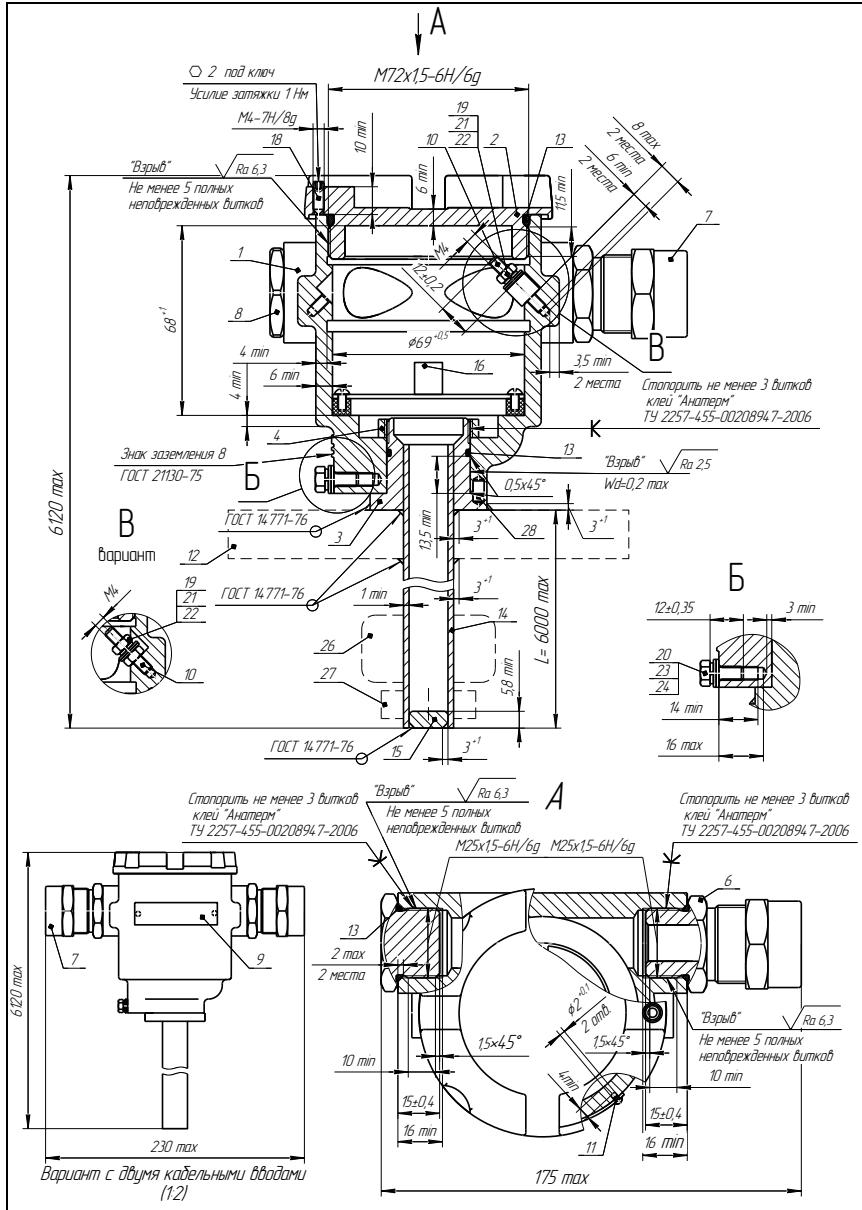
Чертеж средств взрывозащиты для корпуса «Е» («Е-НЖ»)
